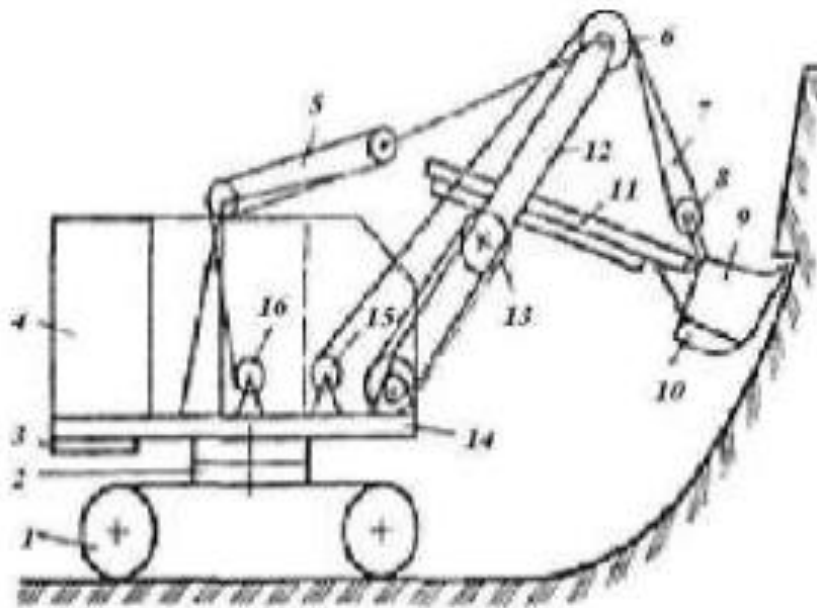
Принципова схема одноковшового екскаватора з робочим обладнанням «пряма лопата»:
